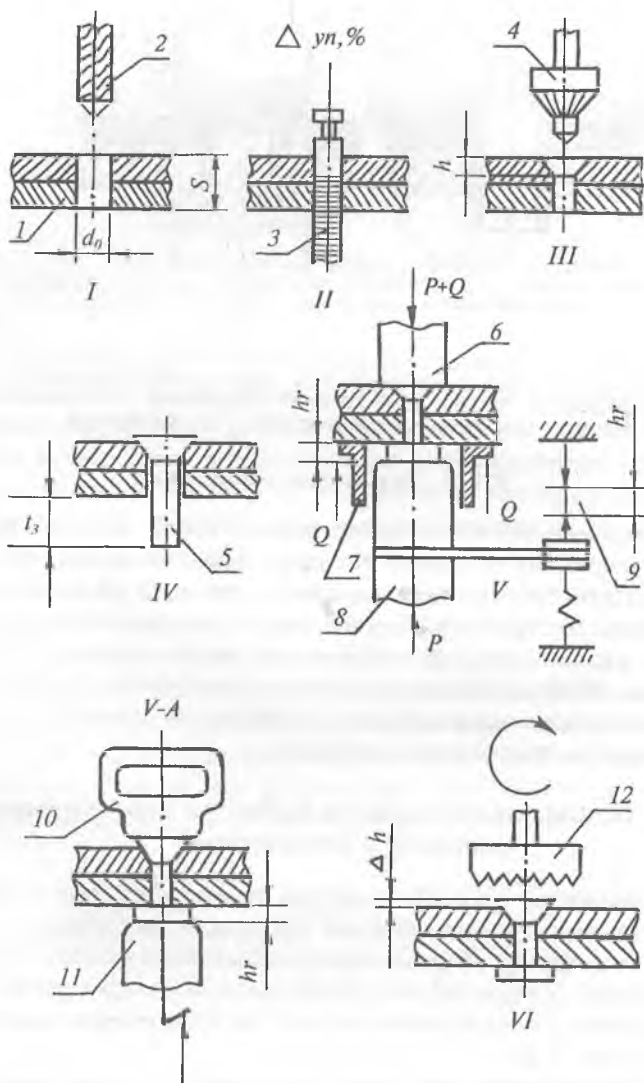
Последовательность операций при выполнении клепальных работ: 1 — деталь; 2 — сверло; 3 — дорн; 4 — зенковка; 5 — заклепка; 6 — верхний пуансон; 7 — прижим; 8 — нижний пуансон; 9 — система микровыключателей; 10 — ручная поддержка; 11 — обжимка пневматического молотка; 12 — торцевая фреза
